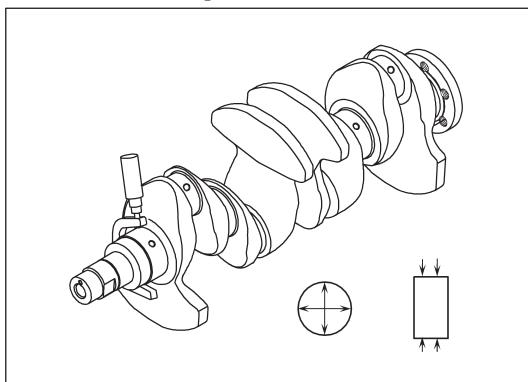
Измерение диаметра шейки коленчатого вала
